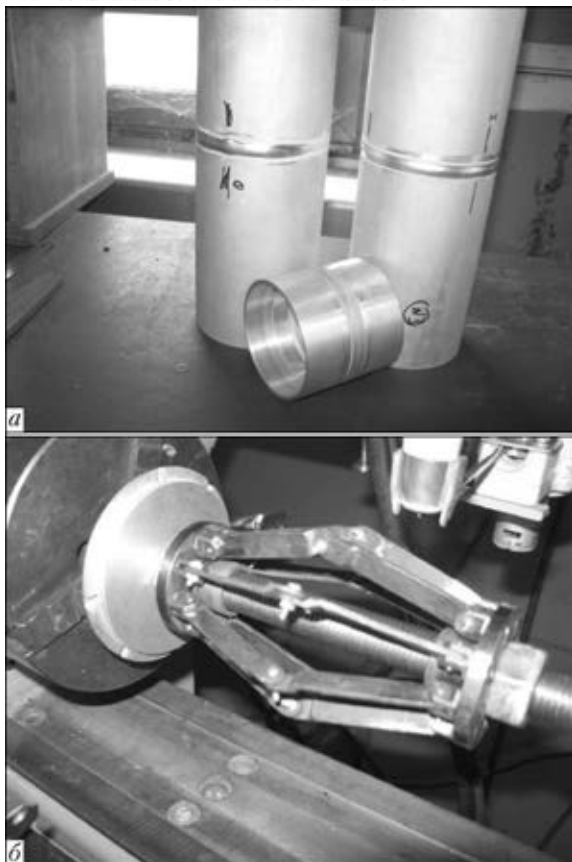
Общий вид образцов кольцевых стыков из сплава АМг6 (а) и сборочное устройство для их сварки (б) (справа — нагружающая гайка)
